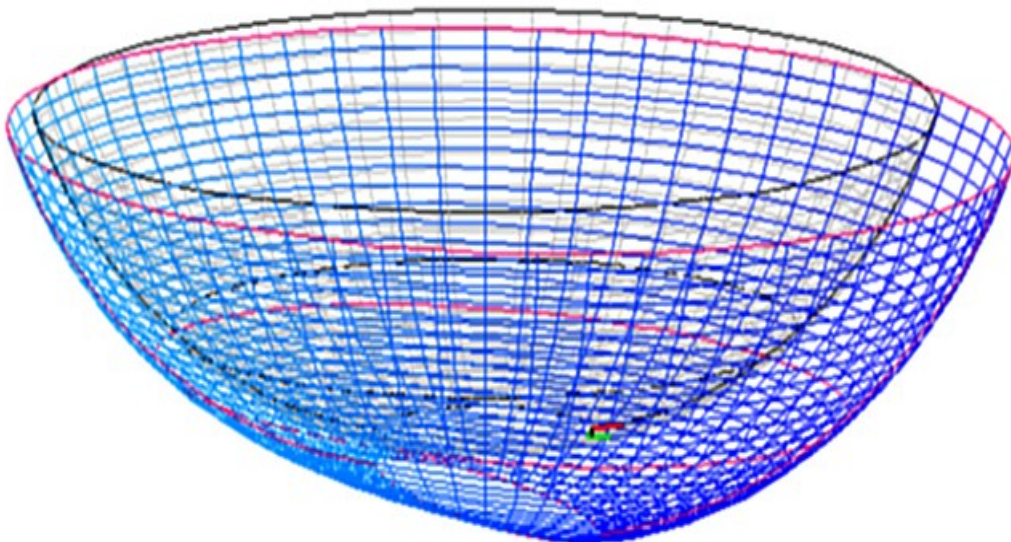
Konkave Lagerschale mit Gegenkörper (dimensionslose Darstellung)
